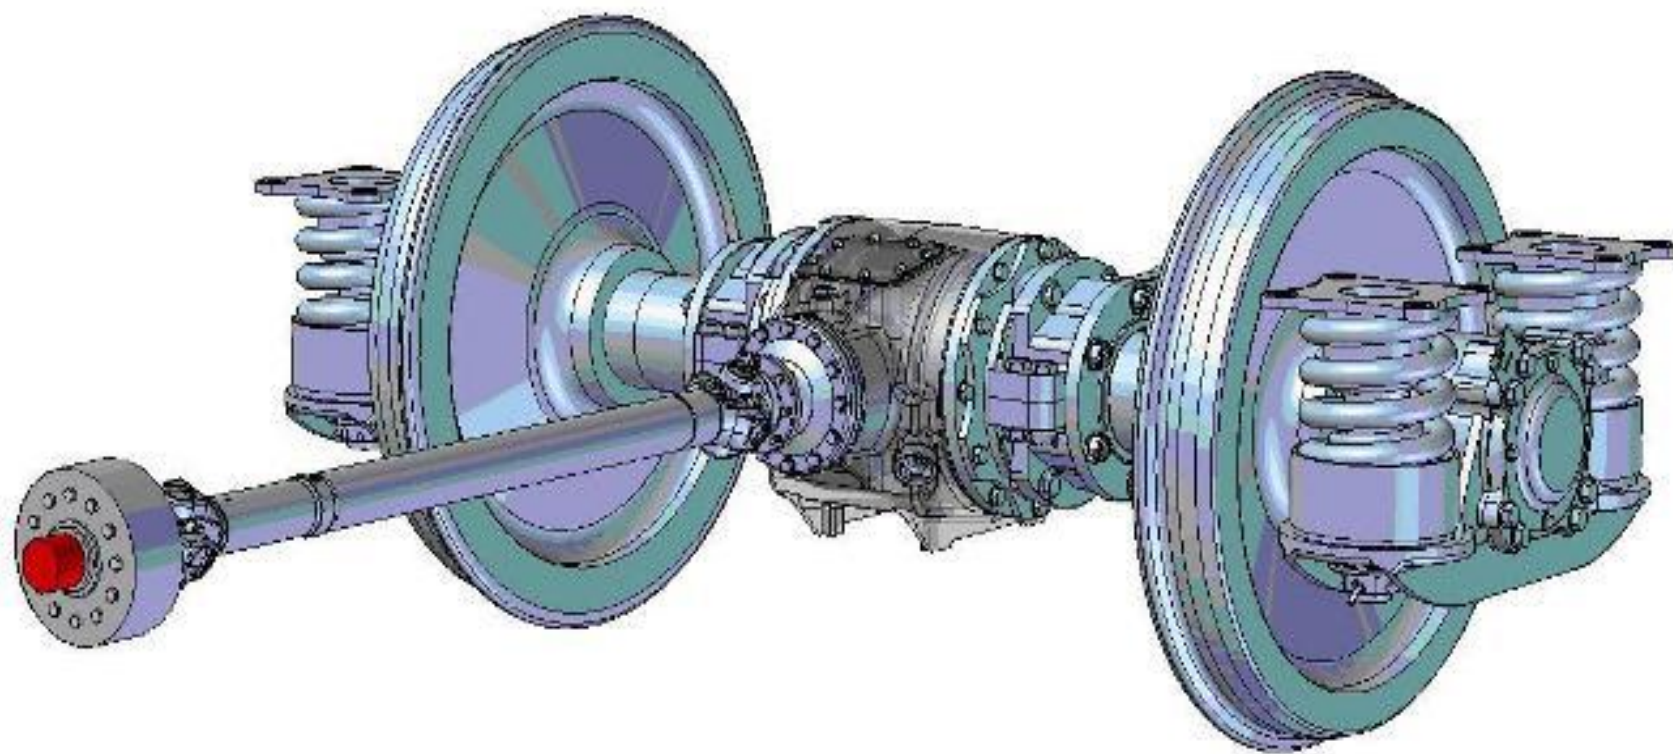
редуктор; 2- карданный вал; 3 - предохранительные устройства;
